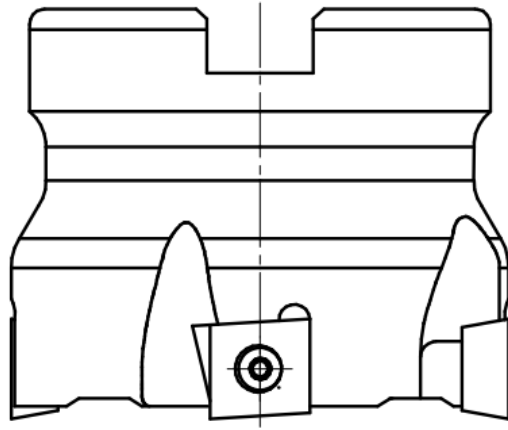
Фреза торцева з тангенціальними пластинами [4]
